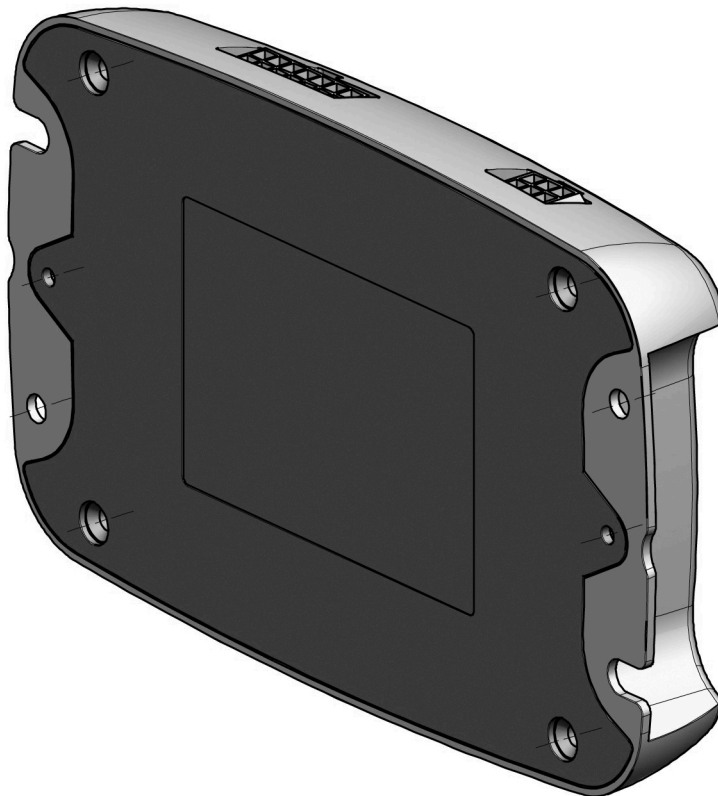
Внешний вид нижней панели корпуса основного блока.
